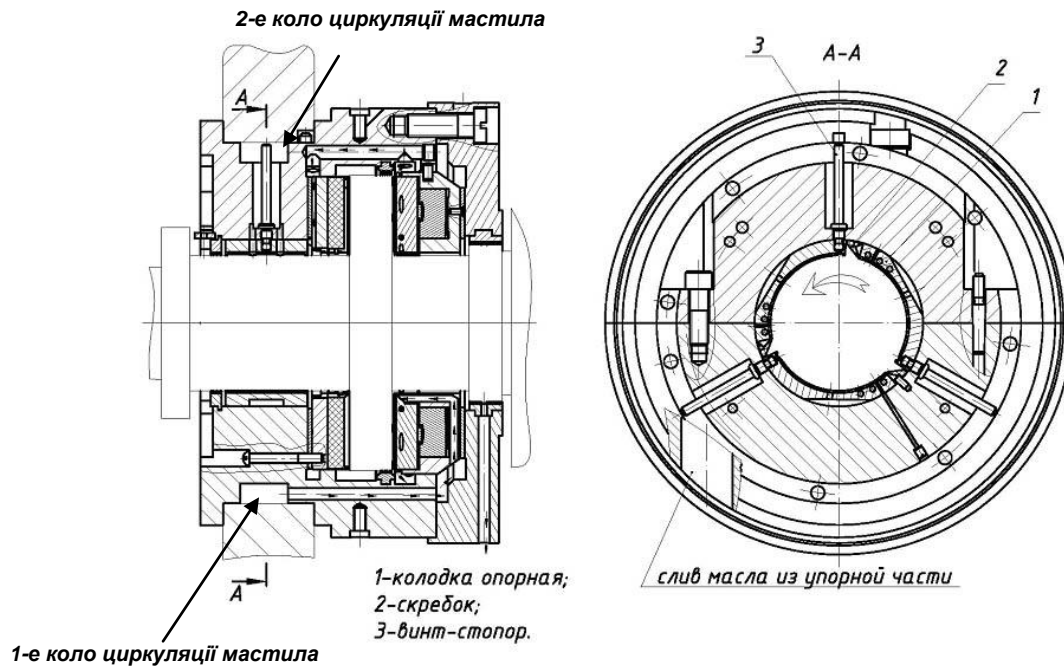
Підшипник опорно-упорний з двома колами циркуляції мастила
